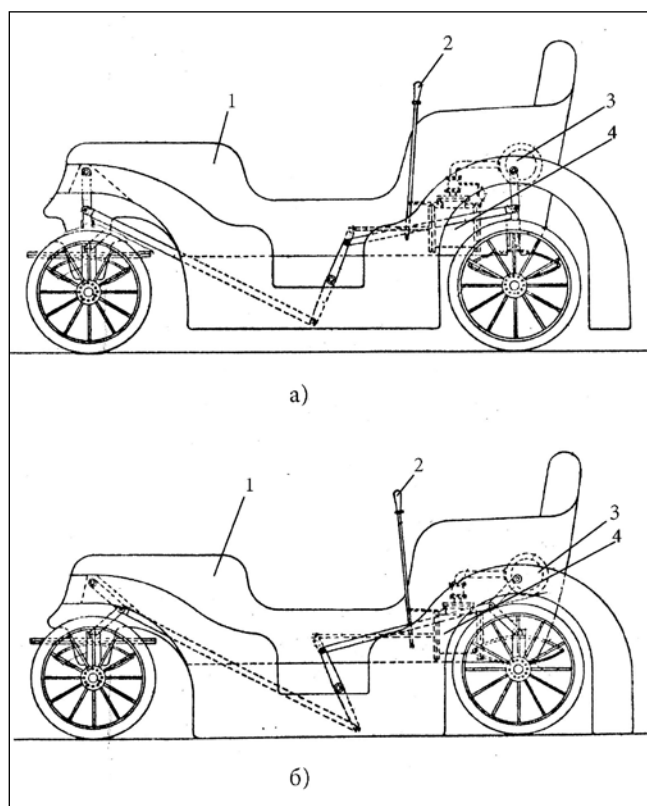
Торможение кузовом. 1 — кузов автомобиля, 2 — тормозной рычаг, 3 — управляющий пневмоцилиндр, 4 — рабочий пневмоцилиндр
